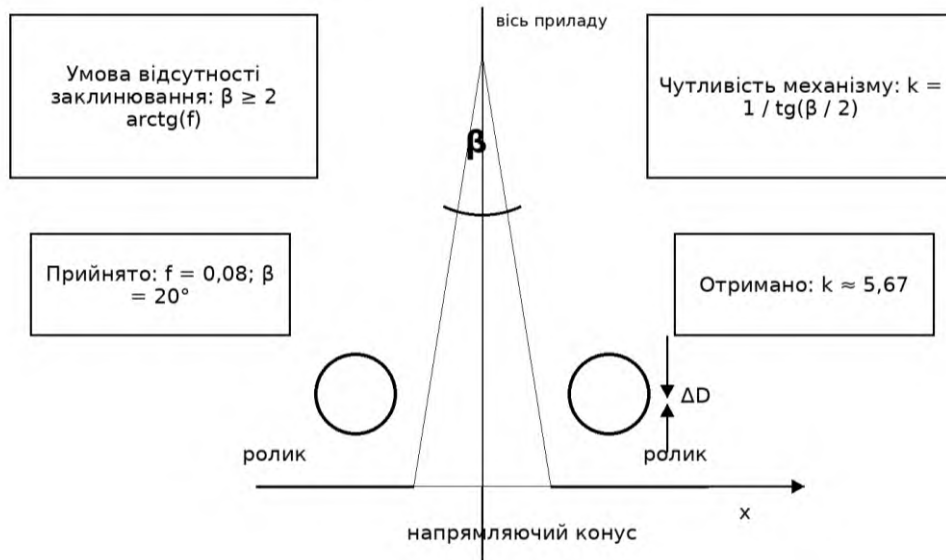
Параметрична схема конусно-роликового вузла
